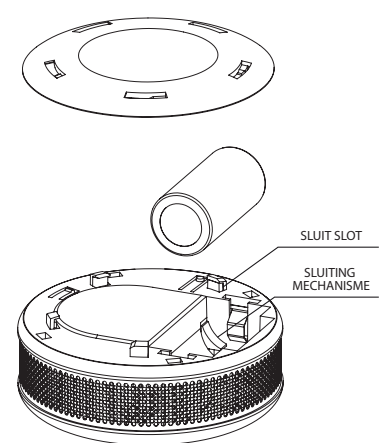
Fibaro Rook Sensor onderaanzicht zonder de batterij geïnstalleerd
